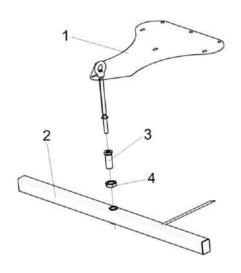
Установка траверсы ЖКС-45-0130000
